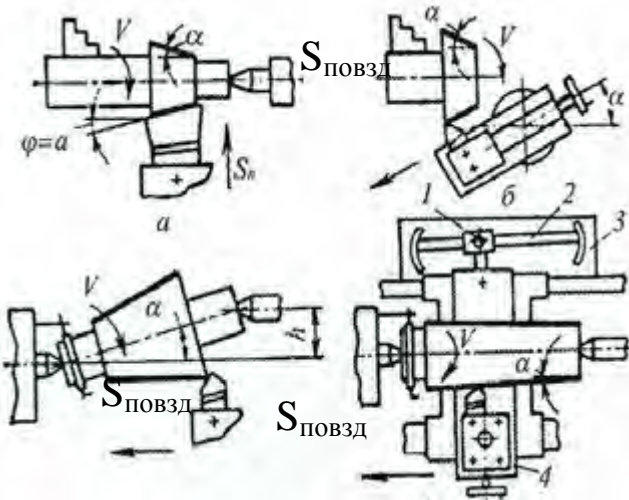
Схеми обточування зовнішніх конічних поверхонь на токарно-гвинторізних верстатах
